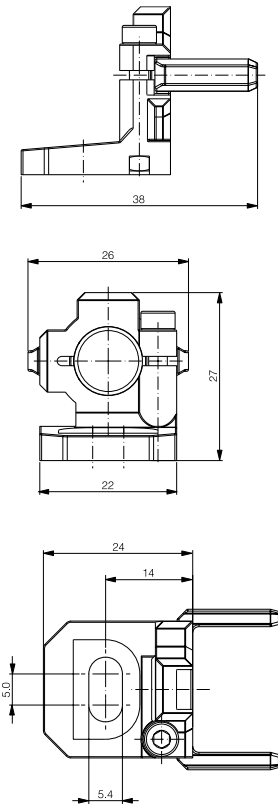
SUPORTE DE FIXAÇÃO PADRÃO SUPERIOR/INFERIOR N.º 5 (REF: YXW-0005-000)
